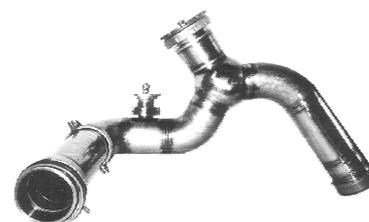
Элемент воздушного трубопровода из сплава OT4-0
